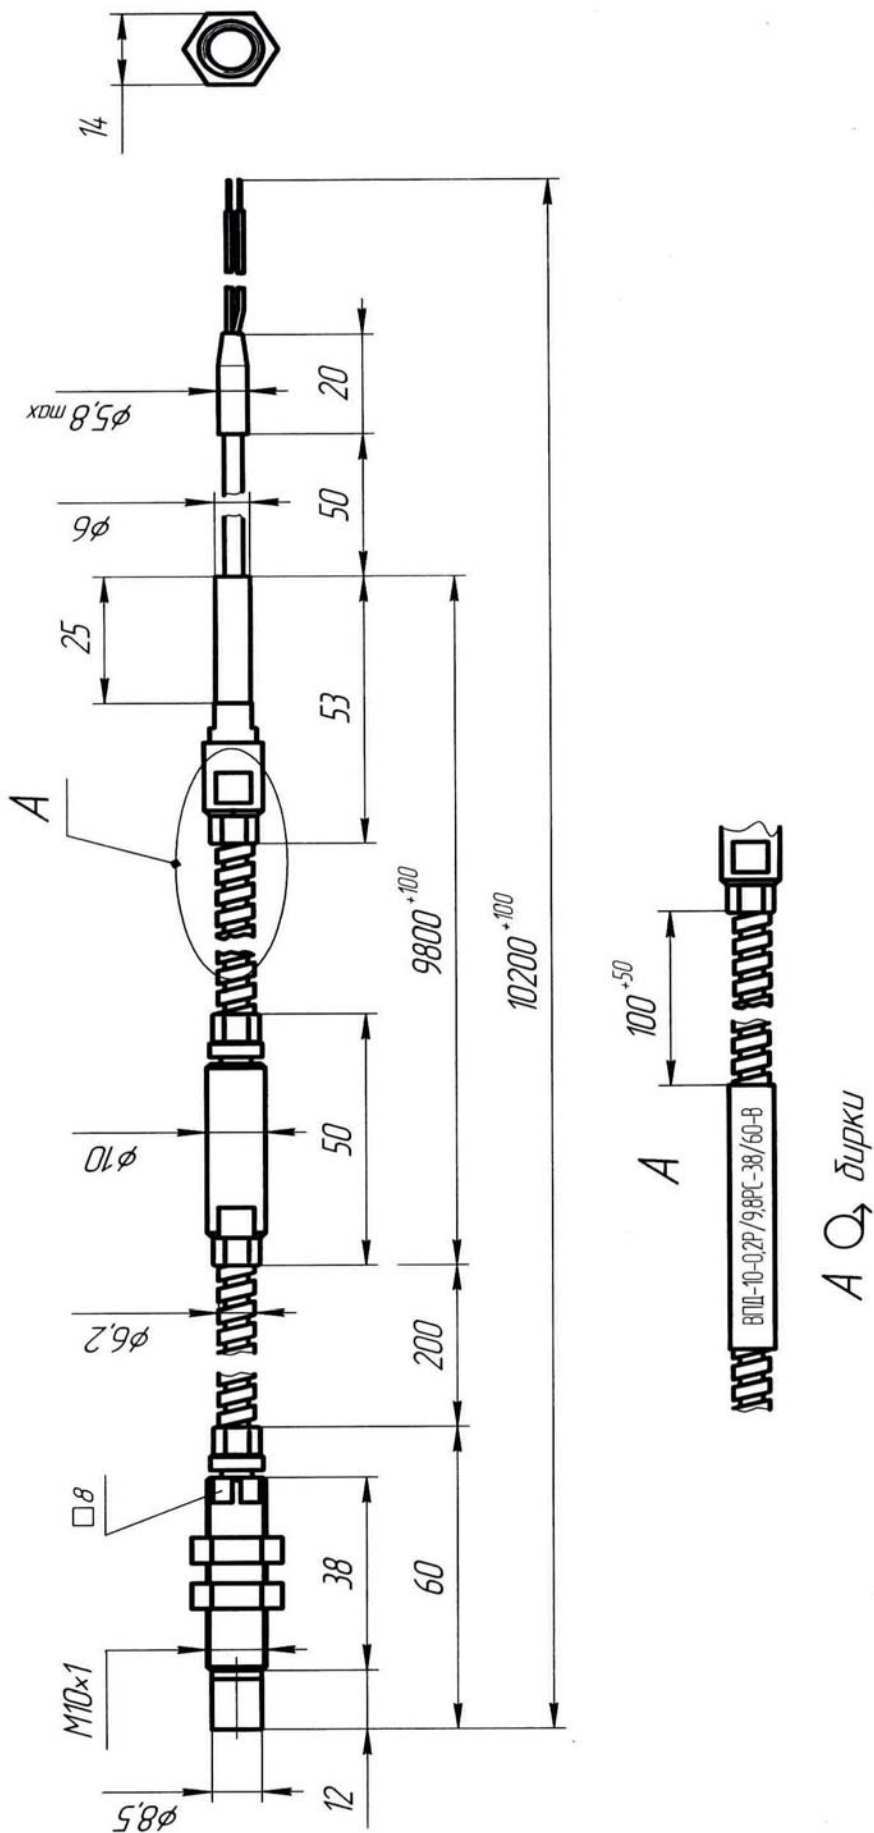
Габаритно-установочные размеры датчика токовихревого ВПД-10-0,05P/9,95PC-28/50-B
